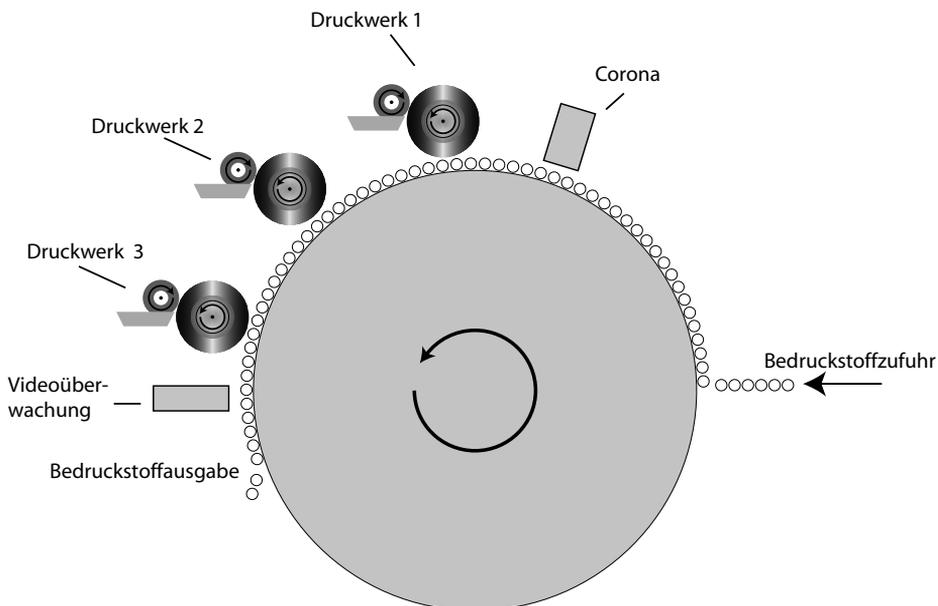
Schemazeichnung Tampoprint Rotoprinter
